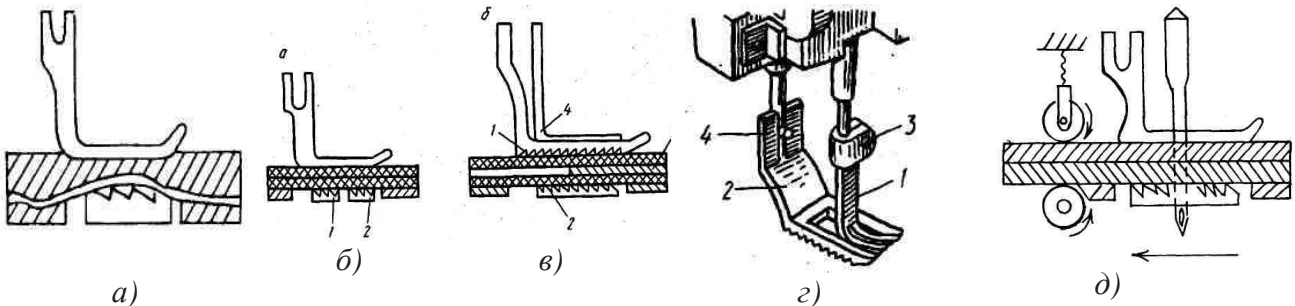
Види механізмів переміщення матеріалів: а) – однорейковий, б) – диференційний, в), –двухрейковий з верхньою і нижньою рейками (1-верхня рейка, 2- нижня рейка, 3 – розподіляюча пластинка, 4-лапка; з) – взаєморозташування лапки з верхньою рейкою (1-лапка, 2-верхня рейка, 3,4 –гвинти кріплення); д) – комбінований.
